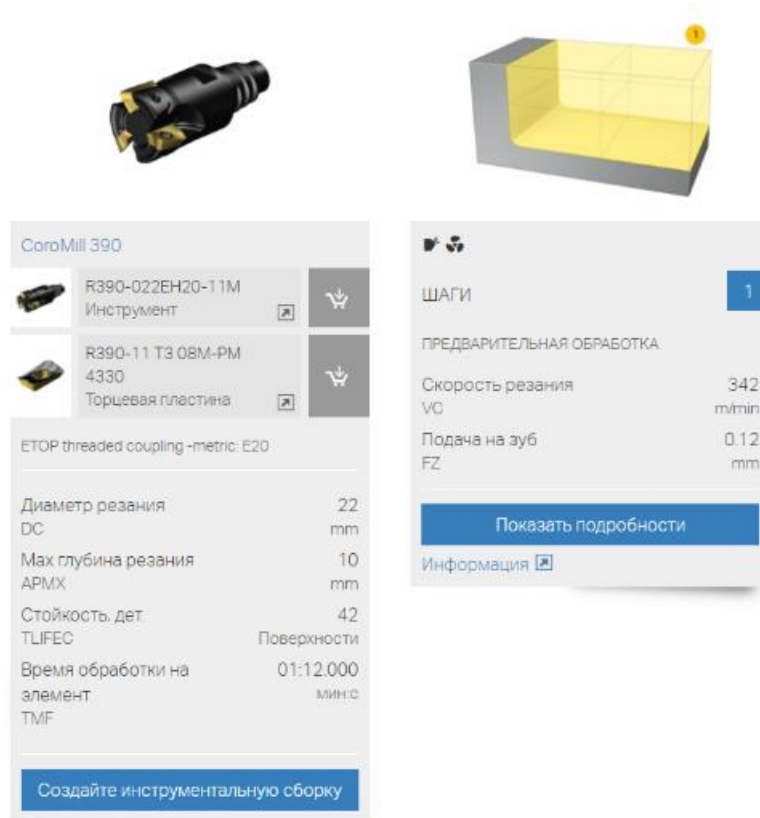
CoroMill 390 R390-022EH20-11M з торцевими пластинками R390-11 T3 08M-PM 4330
